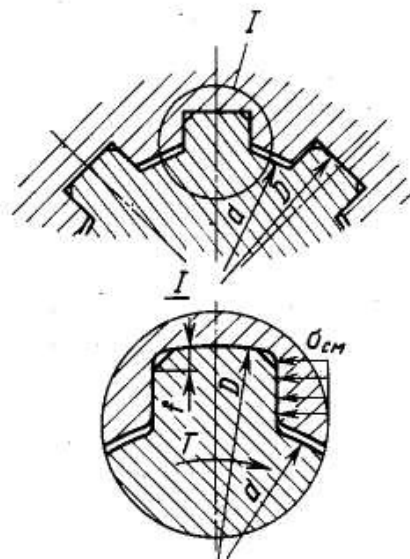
Розрахункова схема зуба шліцевого з'єднання
